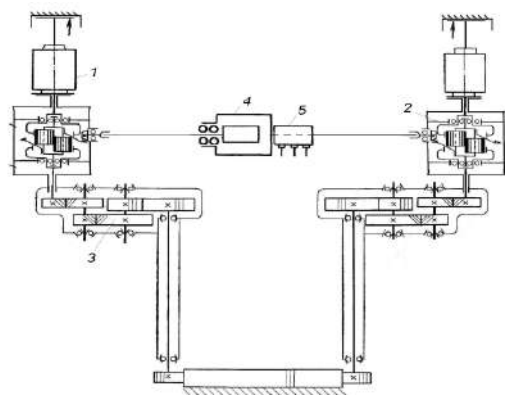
Кинематическая схема двухдвигательного привода механизма поворота драглайна инновационной конструкции: 1 - электродвигатель постоянного тока; 2 - трёхзвенный дифференциал 2К-Н; 3 - редуктор базовой конструкции привода; 4 - гидромашина; 5 - гидроколлектор
